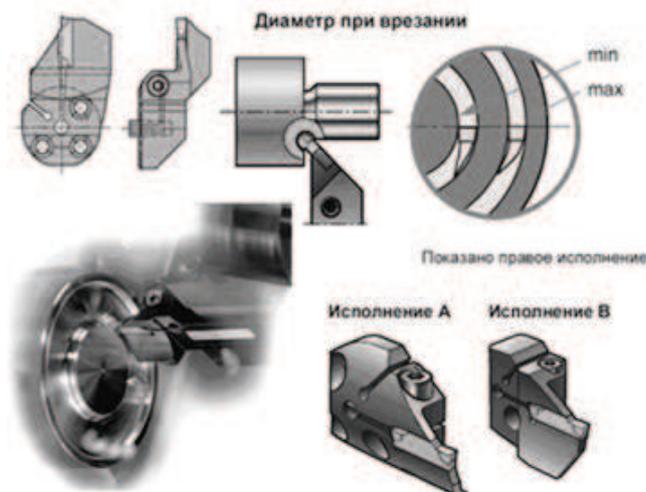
Резцовая головка Sandvik Coromant для обработки торцевых канавок и выборок
